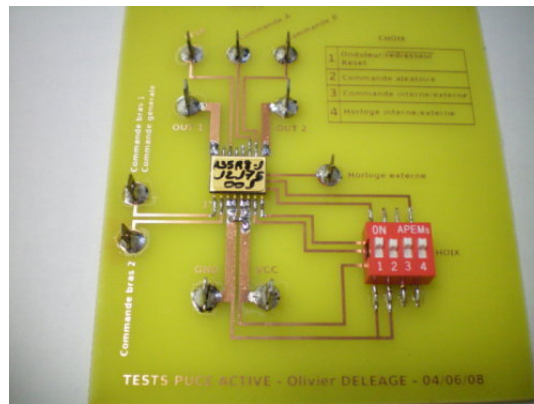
Circuit intégré monté en boîtier sur son PCB d'essais
